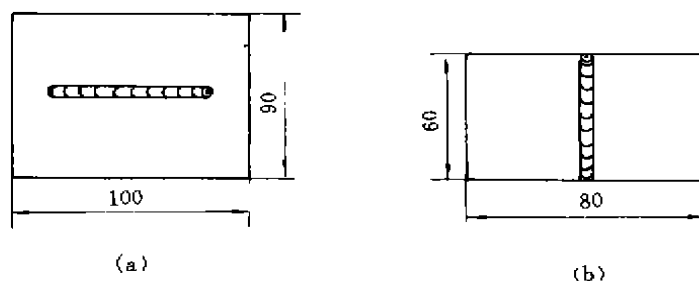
工艺试验试板及接头形式,(a) 堆焊,(b) 对接
